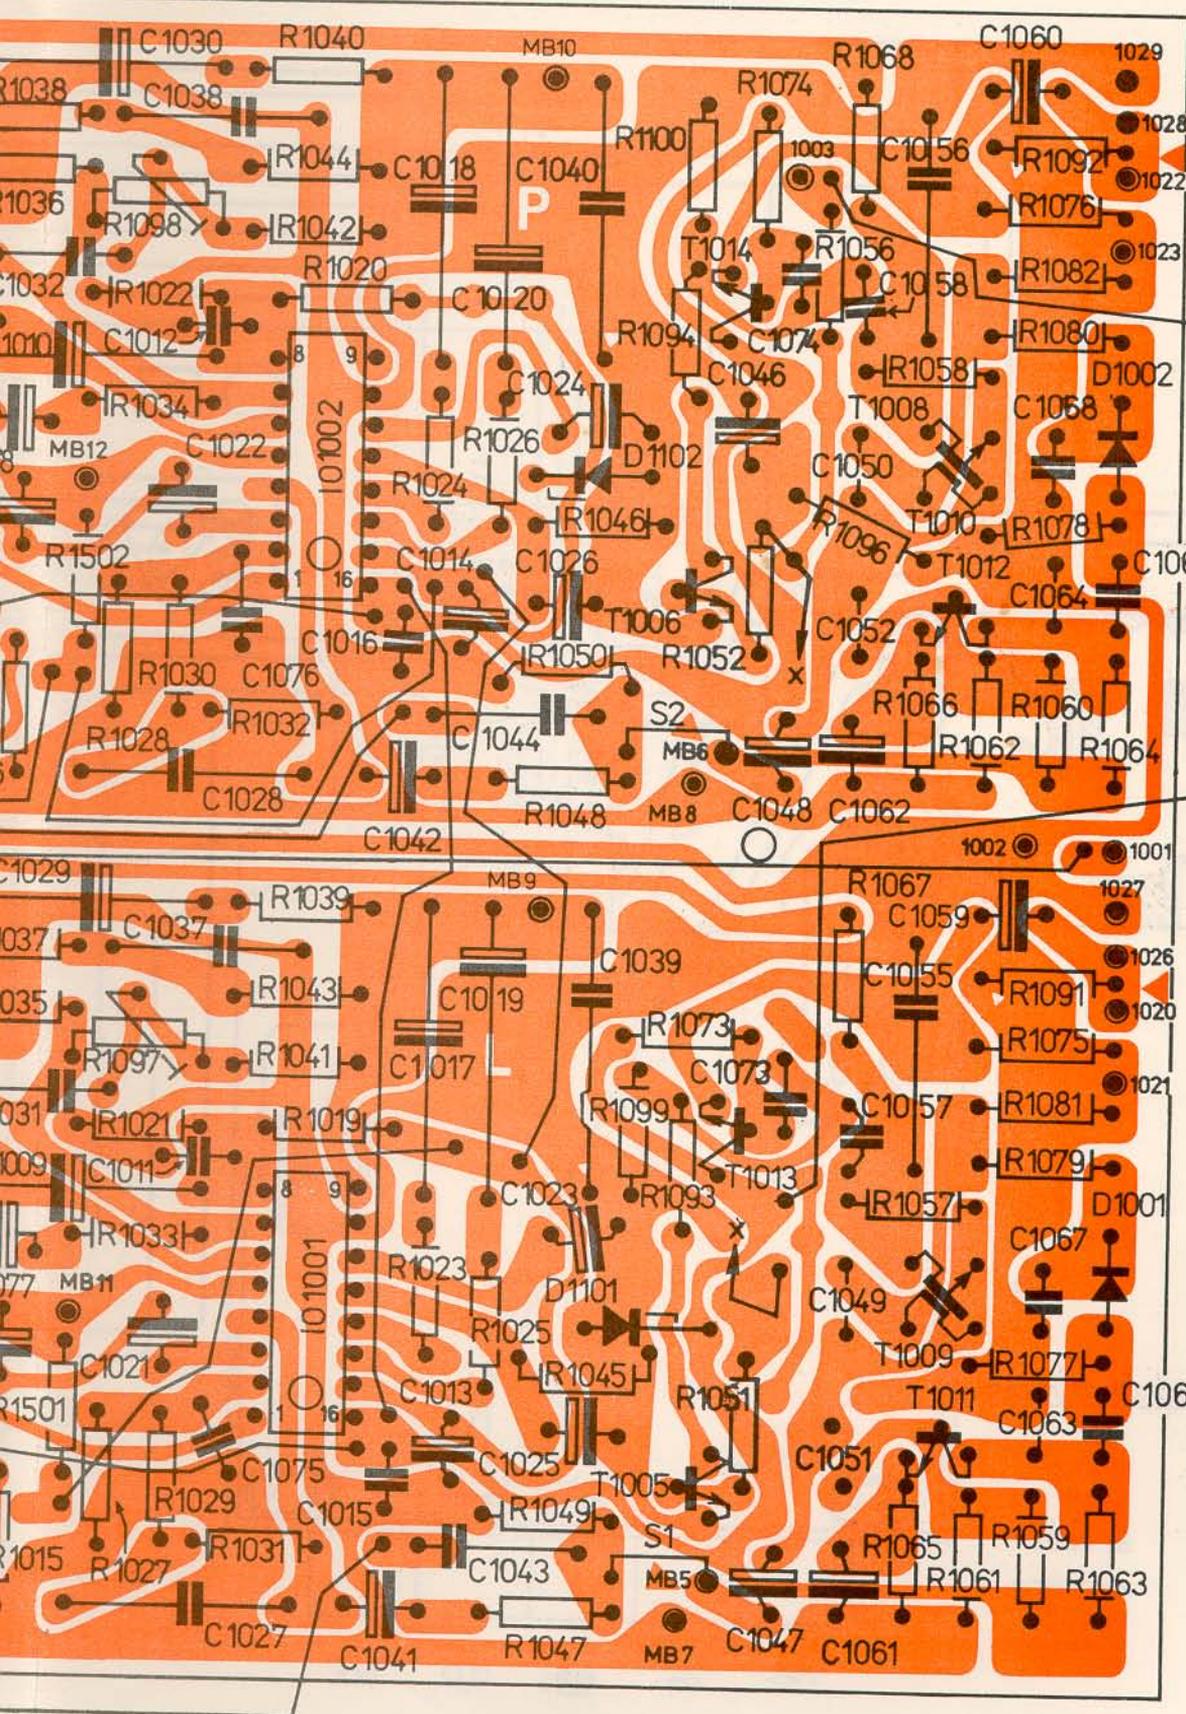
Montážní zapojení stabilizátoru pro magnetofon
